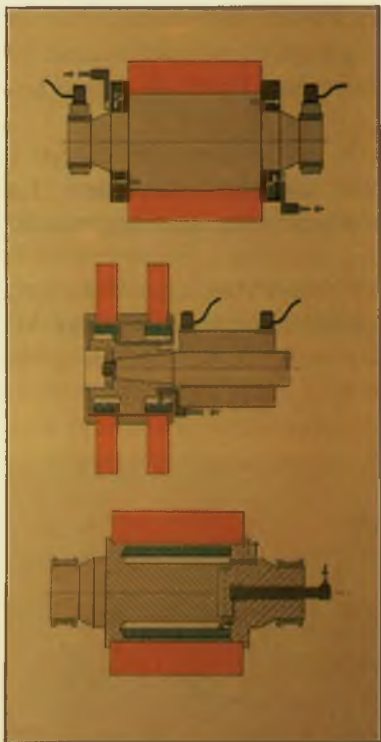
Equilibrado en un plano. Integración del husillo en rectificadoras sin centros.
